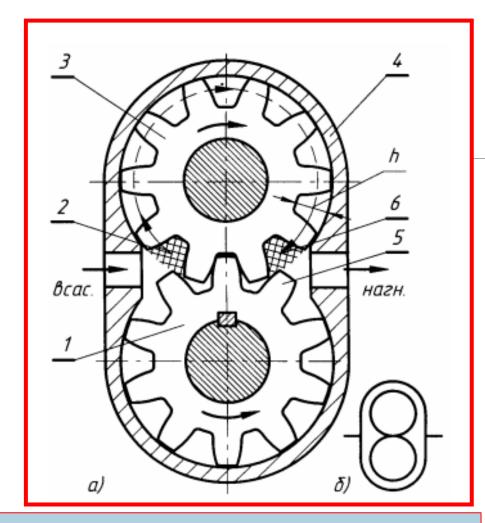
Шестеренный насос: а) конструктивная схема; б) условное обозначение
